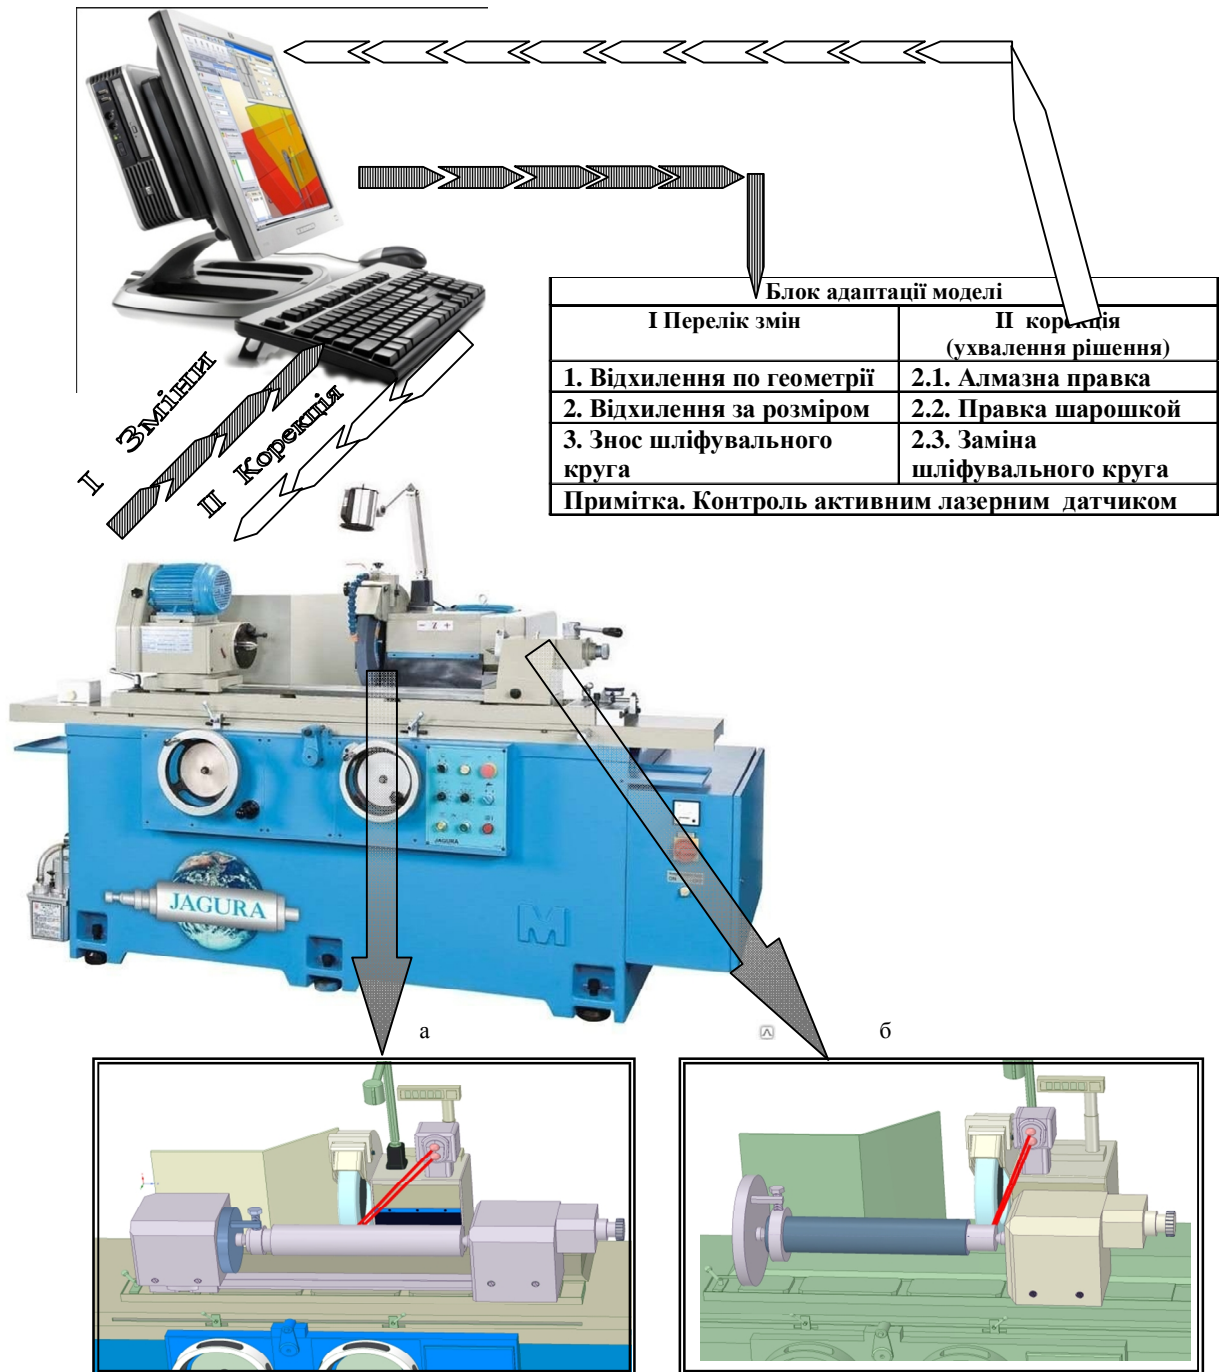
Модель шліфувальної обробки направляючої колонки штампа з активним лазерним контролем
